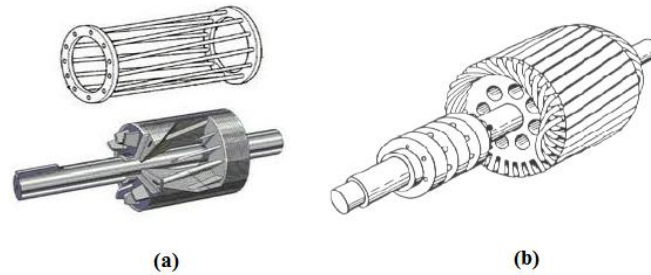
(a) Rotor jaula de ardilla, (b) Rotor bobinado (Vidal J, 2002,30).
